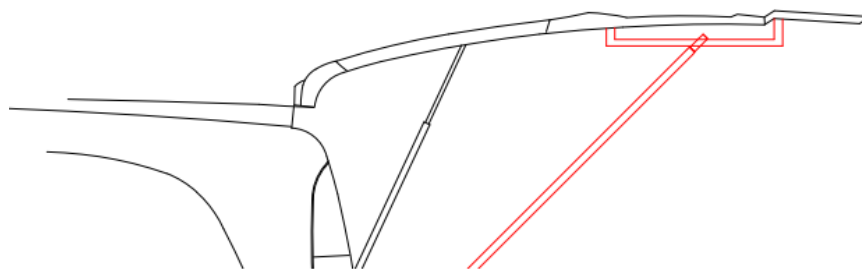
Croquis del segon plantejament. FONT: Pròpia elaborada amb AutoCAD 2014.
